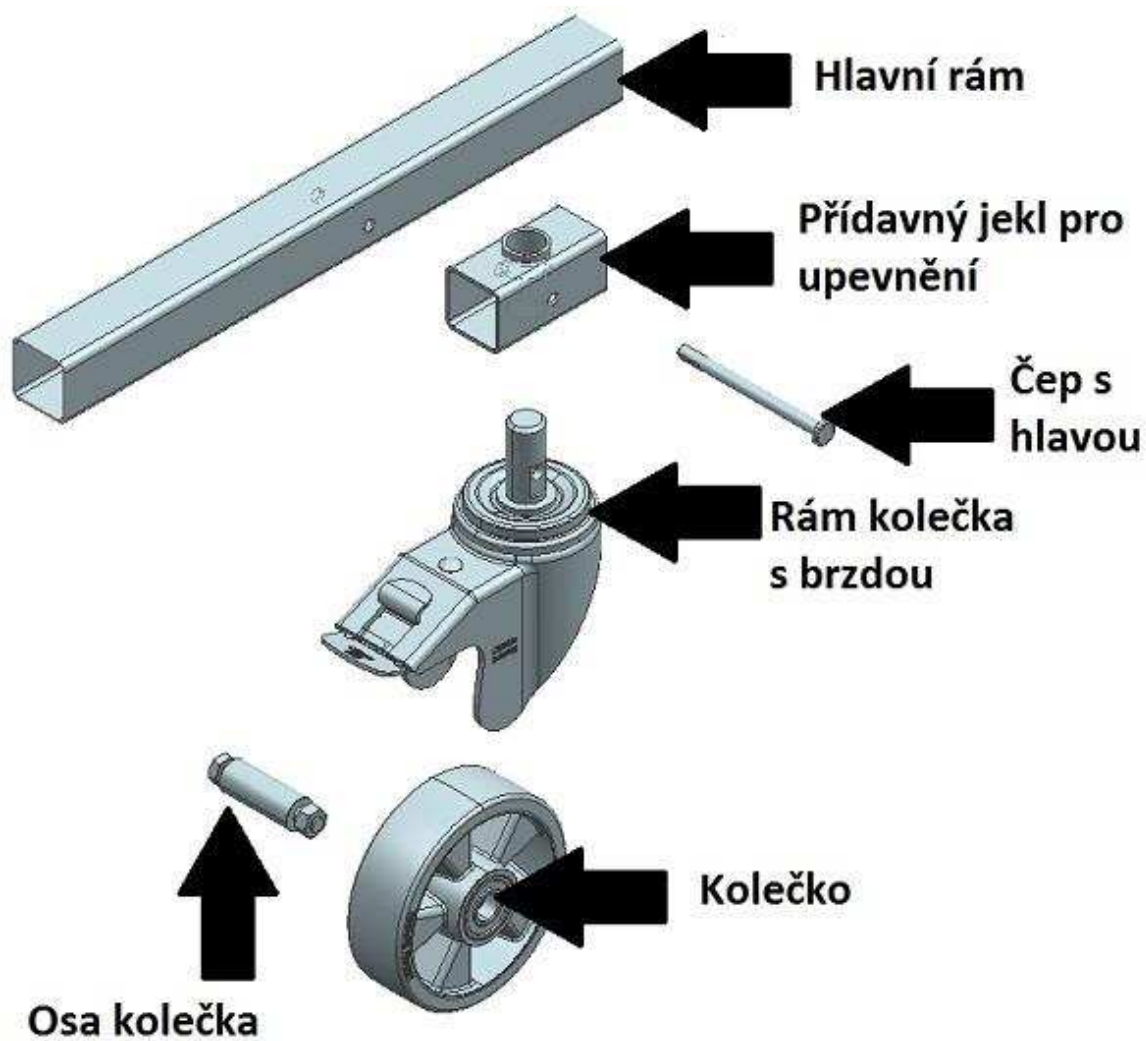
Detailní půdorysný pohled na upevnění kolečka
